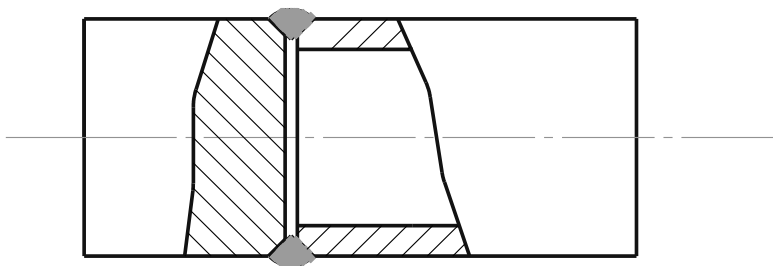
Сварка трубы со стержнем встык с предварительным разделением кромок
